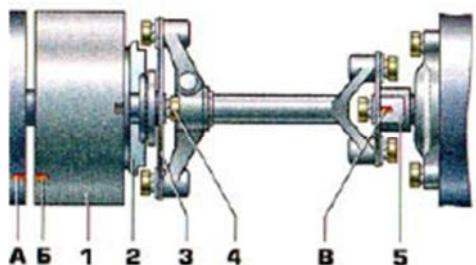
Привод муфты опережения впрыска топлива на автомобиле КамАЗ: А - метка на корпусе ТНВД; Б - метка на муфте опережения впрыска; В - метка на заднем фланце ведущей полумуфты приводы; 1 - автоматическая муфта опережения впрыска топлива; 2 - ведомая полумуфта привода; 3 - фланец ведомой полумуфты привода; 4 - болт; 5 - задний фланец ведущей полумуфты привода
